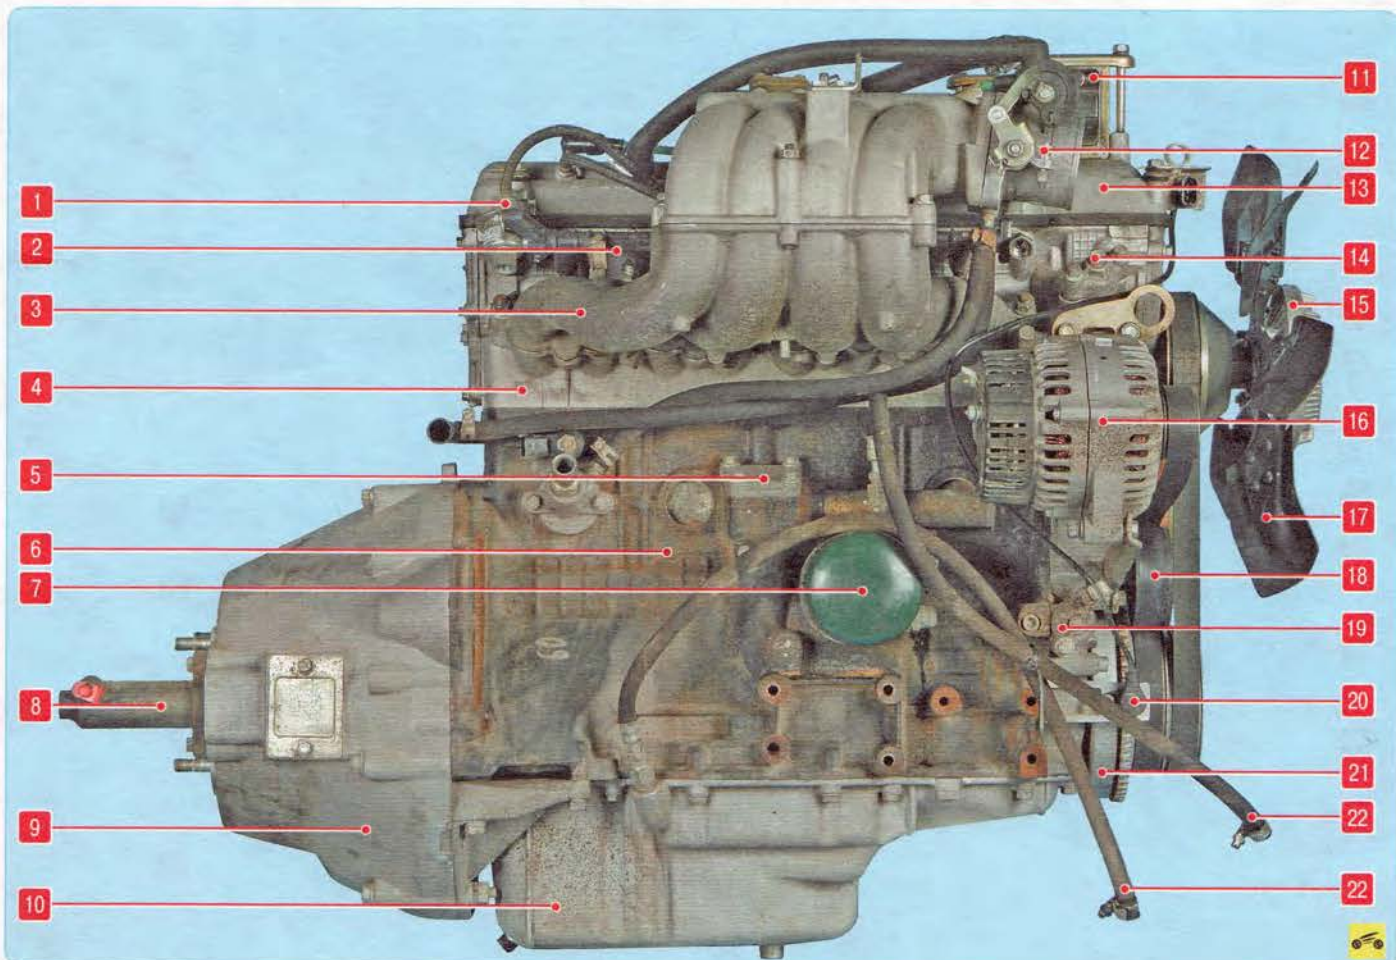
Двигатель 3М3-409 (вид справа): 1 – регулятор давления топлива; 2 – топливная рампа; 3 – впускная труба; 4 – головка блока цилиндров; 5 – крышка промежуточного вала; 6 – блок цилиндров; 7 – масляный фильтр; 8 – рабочий цилиндр привода выключения сцепления; 9 – картер сцепления; 10 – масляный картер; 11 – катушка зажигания; 12 – дроссельный узел; 13 – крышка головки блока цилиндров; 14, 19 – гидронатяжители; 15 – вязкостная муфта; 16 – генератор; 17 – вентилятор; 18 – натяжной ролик; 20 – датчик положения коленчатого вала; 21 – шкив коленчатого вала; 22 – шланги масляного радиатора
